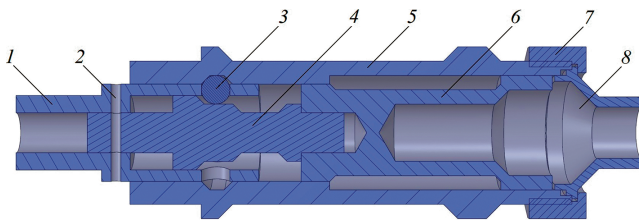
Конструктивная схема замкового устройства шарикового типа: 1 – шток; 2 – срезная шпилька; 3 – шарик; 4 – толкатель; 5 – корпус; 6 – поршень; 7 – прижимная гайка; 8 – штуцер
